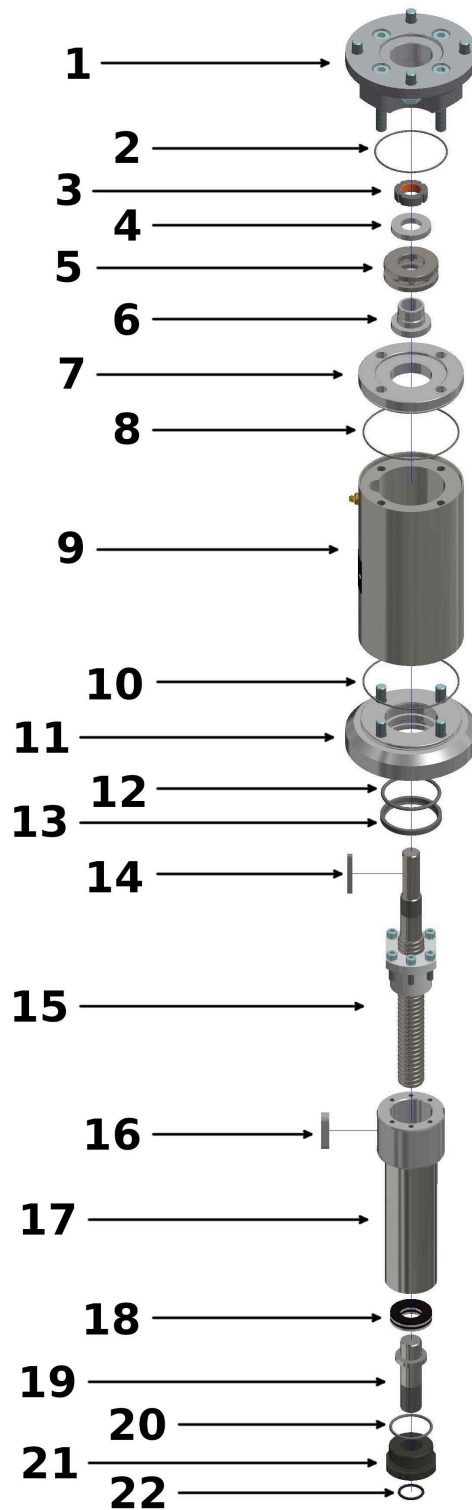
Explosionszeichnung der Schubeinheit. Bauteilbezeichnungen sind in der Tabelle 2 ersichtlich.
